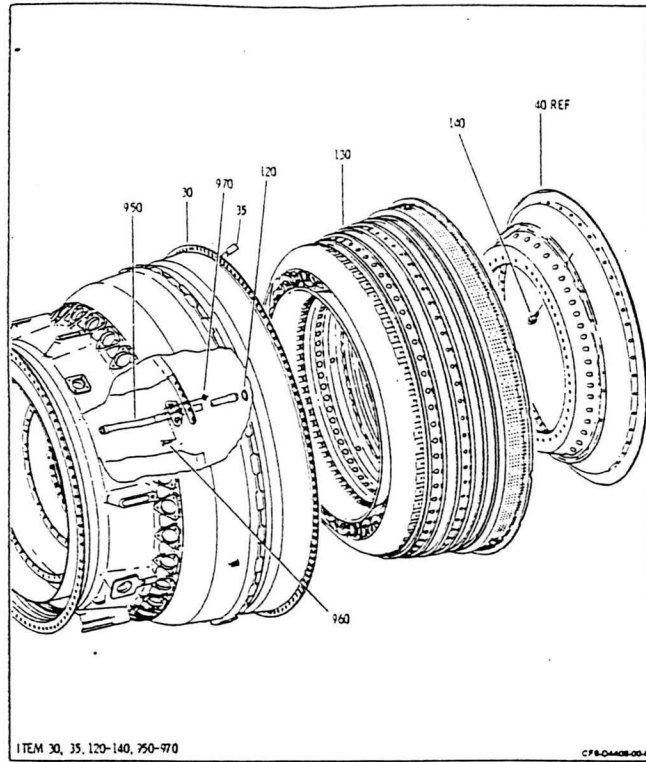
แสดงภาพ 4 B Module (High Pressure Compressor Stator Assembly)
